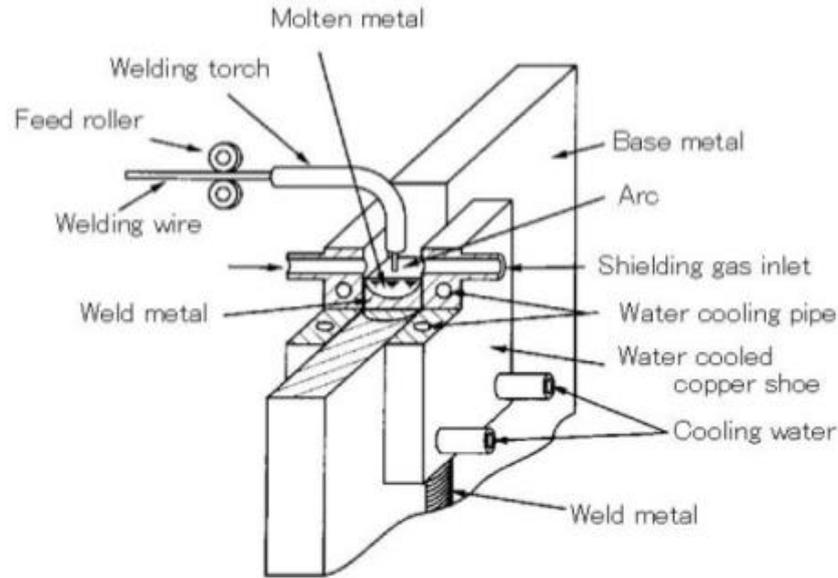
Esquema soldadura eléctrica por gas (Fuente: slideshare.net)
